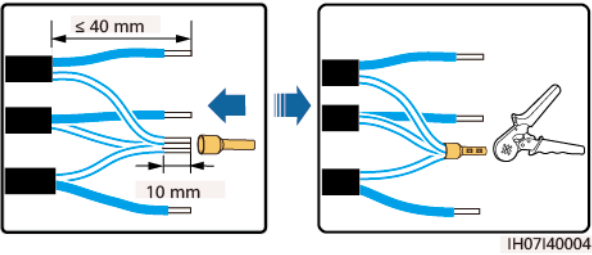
Montagem de um conector de sinal (SUN2000 único)
